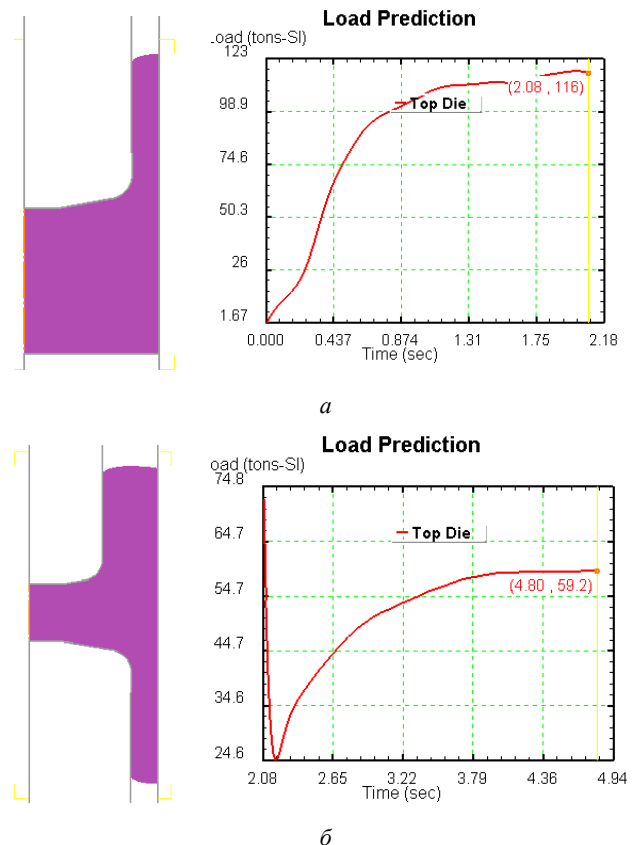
Послідовне зворотне видавлювання порожнин з кантуванням заготовки: а – формування порожнини більшого діаметру та діаграма зусилля; б – формування порожнини меншого діаметру після кантування (перевороту) заготовки та діаграма зусилля
